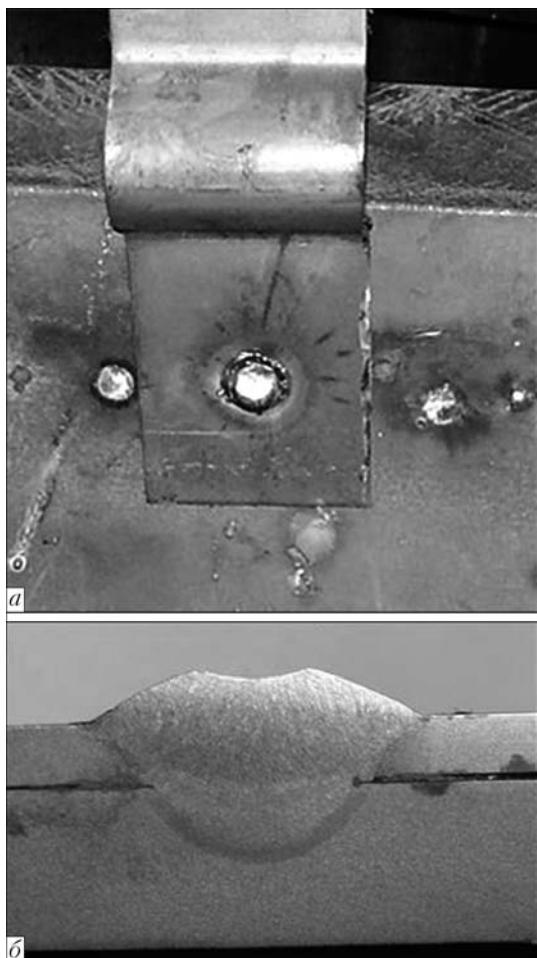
Внешний вид сварного точечного соединения, полученного ДТС в вертикальном положении (а) и его макрошлиф (б)
